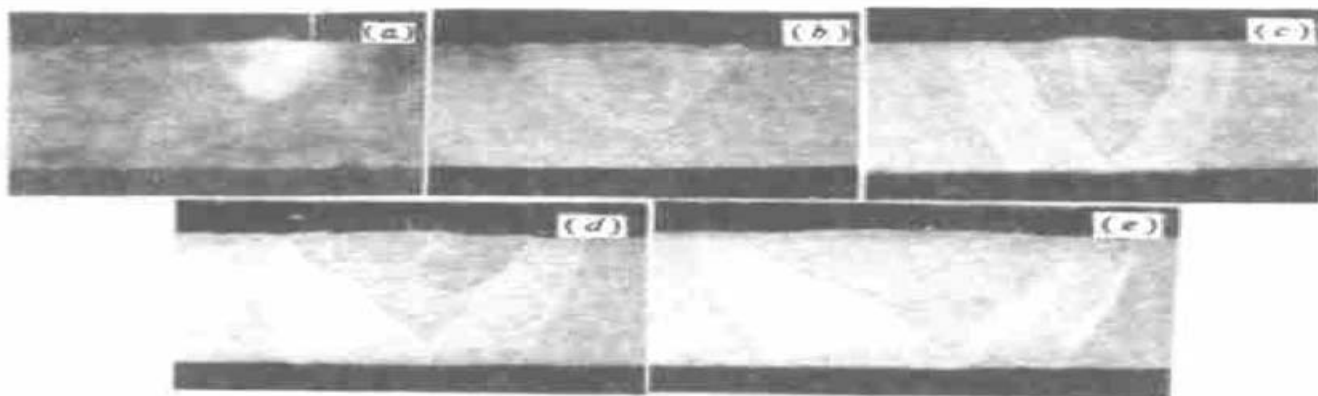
焊速 V 不同时的焊接断面组合照片
